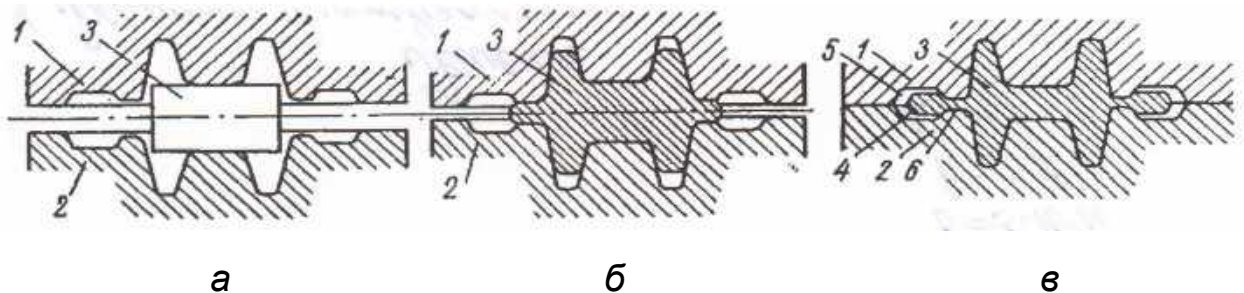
Схема заповнення струмків штампа при гарячому об'ємному штампуванні: а – початкове положення; б – проміжне положення; в – положення зімкнутого штампа (1, 2 – верхній і нижній штампи; 3 – заготовка; 4 – облой; 5 – облойна канавка; 6 – місток)
